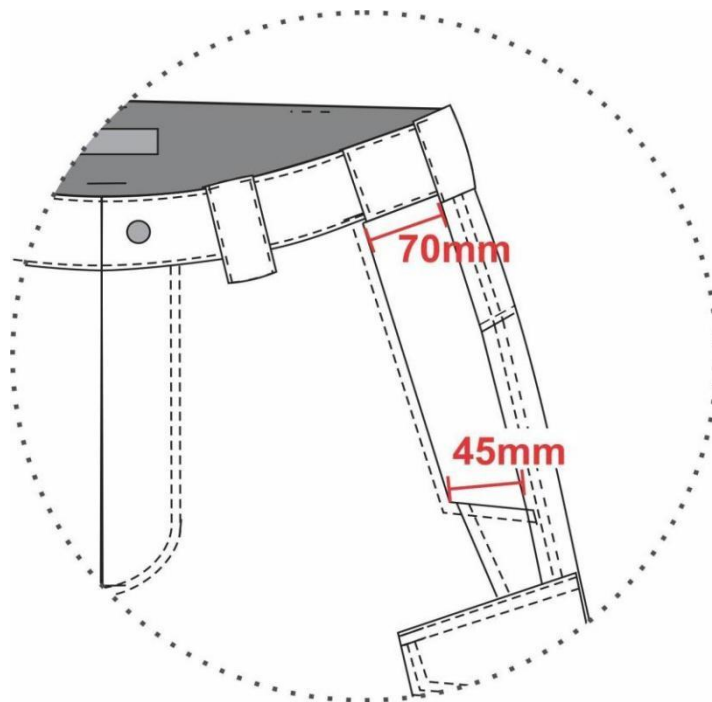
Detalhes do cós e dos passantes traseiro (medida em mm)
